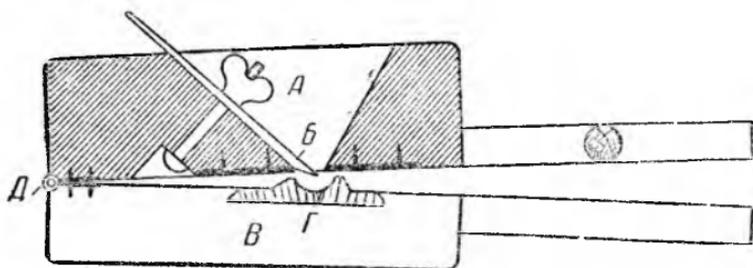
Приспособление для обточки бильярдных киев и других конусных деталей
